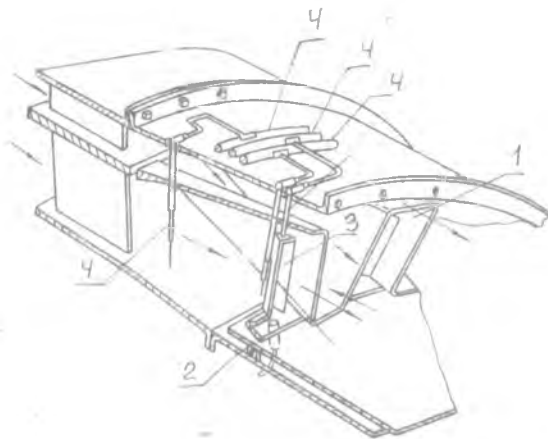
Форсажная камера двигателя с $m \geq 1,5$:
